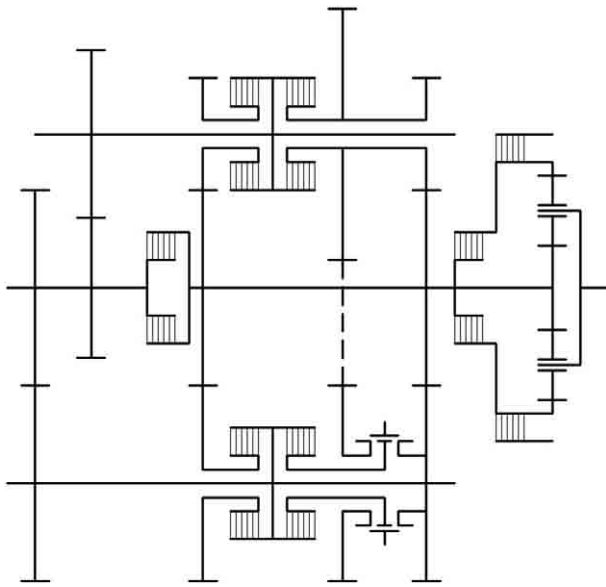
Кинематическая схема девятиступенчатой ГМП компании General Motors
